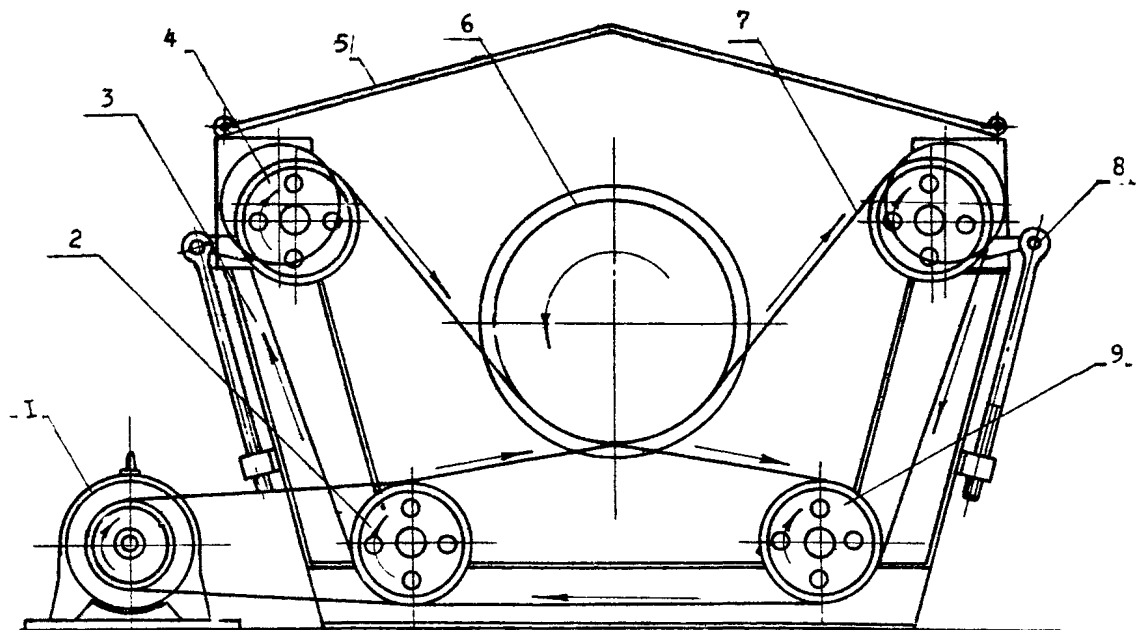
Центрифуга ременная. 1 - электродвигатель, 2 - шкив ведущего вала, 3 - станина, 4 - верхний шкив, 5- верхний щит, 6 - форма, 7 - ремень, 8 - винт подъема верхнего шкива, 9 - шкив ведомого вала.
